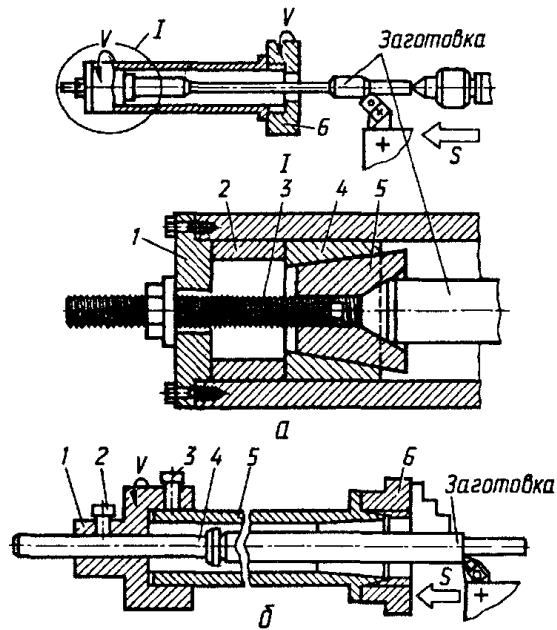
Шпиндельні упори для необроблюваного боку пруткової заготовки: а – упор у обертовий шпиндельний центр: 1 – фланець; 2 – мірна втулка; 3 – гвинт затяжки обертового центру; 4 – розтискна втулка (цанга); 5 – обертовий центр, б – патрон; б - упор у висувну упорну штангу: 1 – муфта, закріплена на задньому кінці шпинделя, 2 - гвинт затиску штанги, 3 - гвинт затиску муфти на шпинделі; 4 - упорна штанга, 5 – шпиндель, б – патрон
